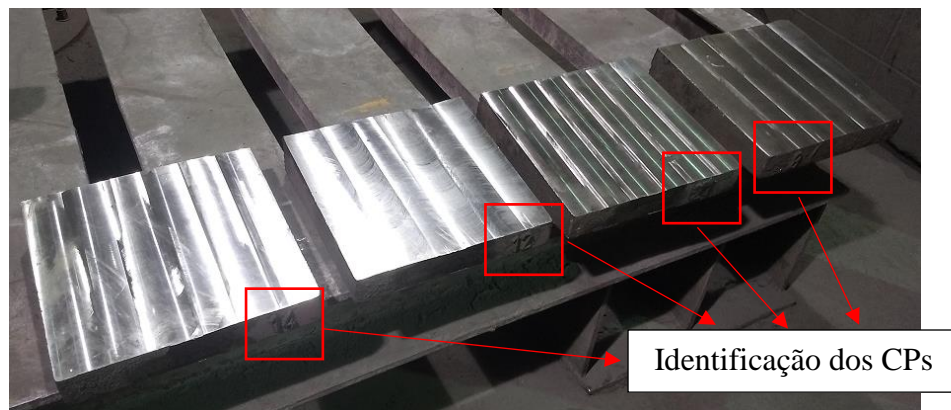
Limpeza das faces e identificação dos corpos de prova para ensaio de líquido penetrante
